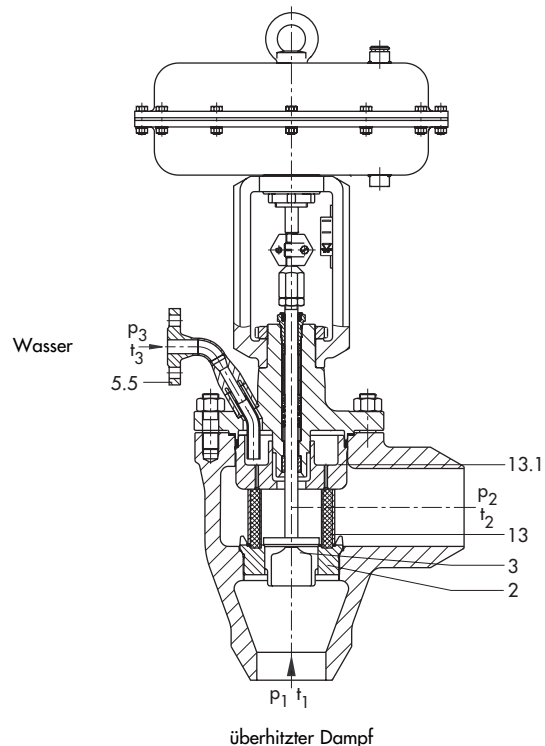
· Pneumatischer Dampfumformer Typ 3286-1 mit Anschweißenden und Antrieb Typ 3271
